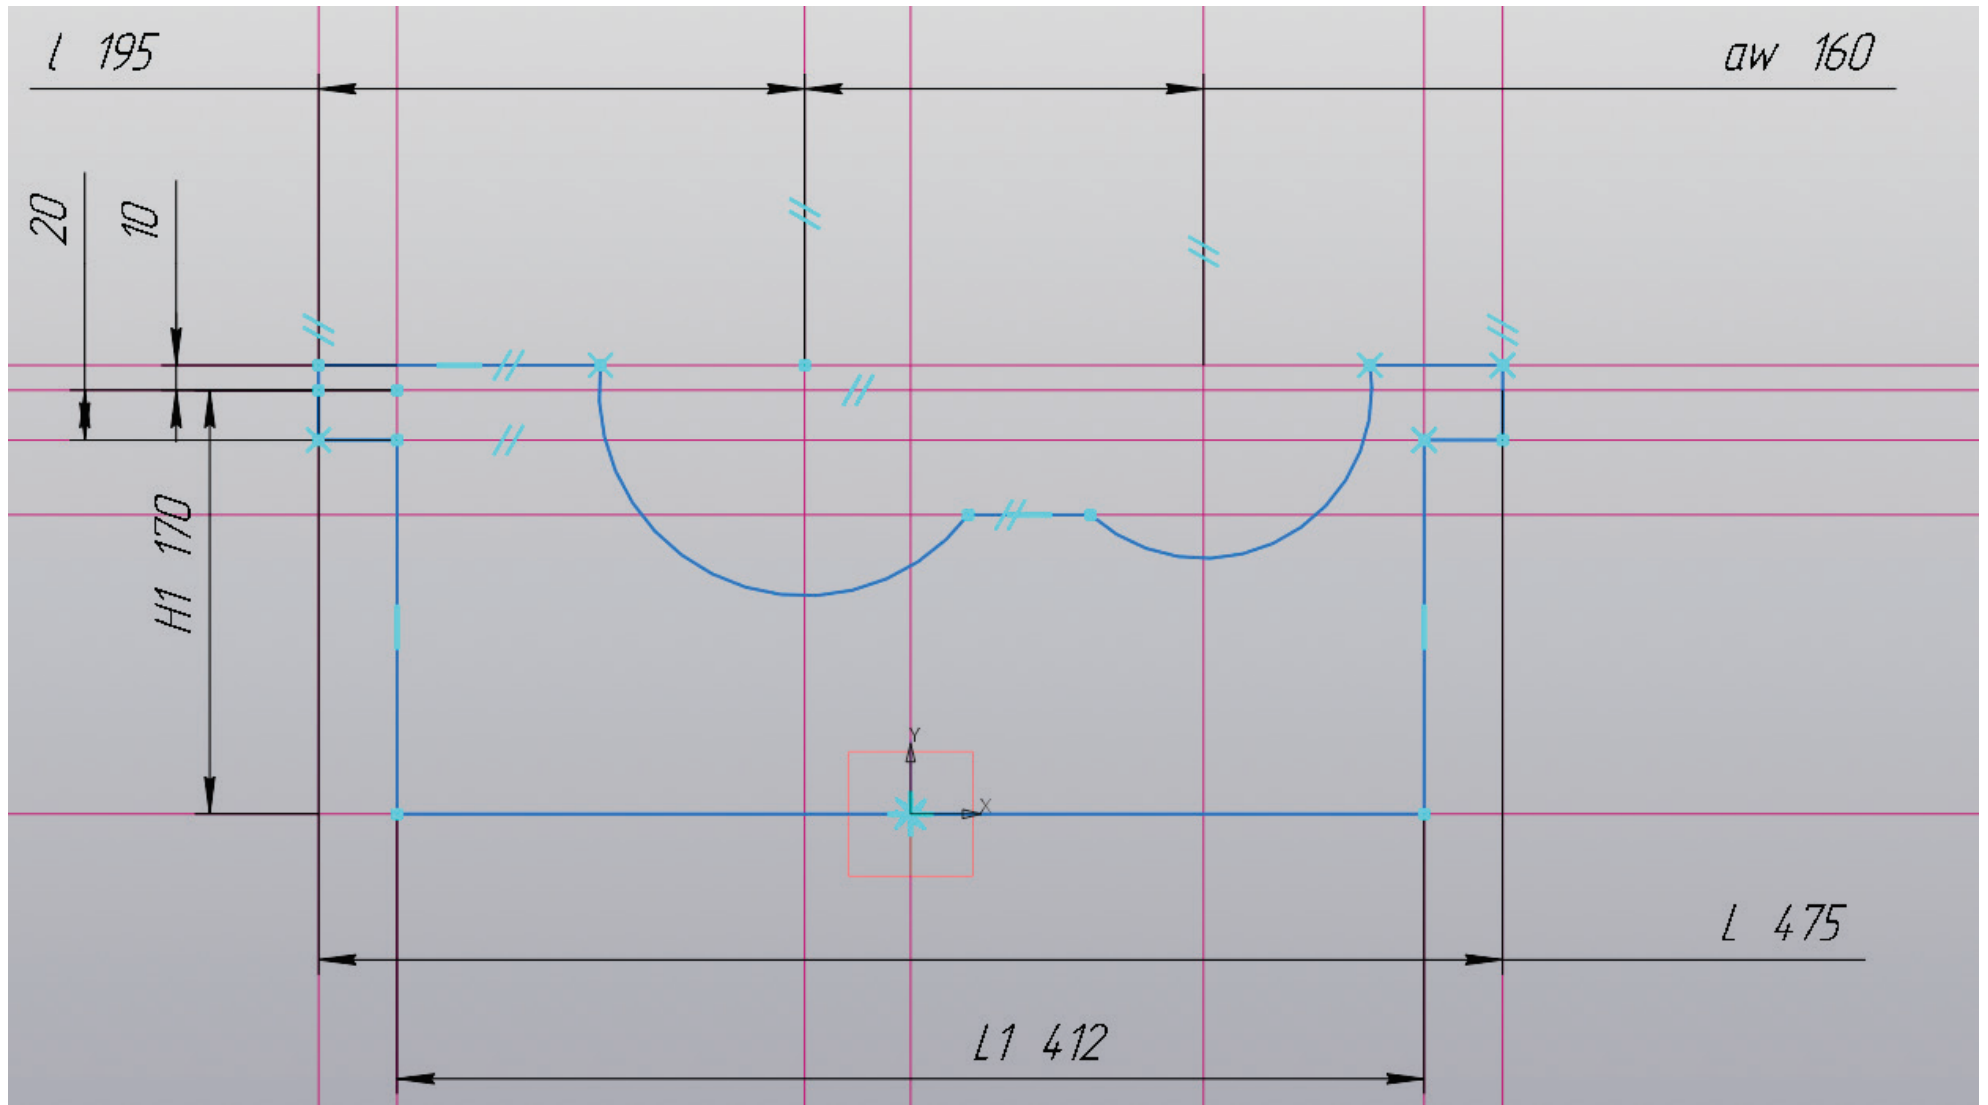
Редуктор цилиндрический, работа с эскизом, создание контура нижней части редуктора
